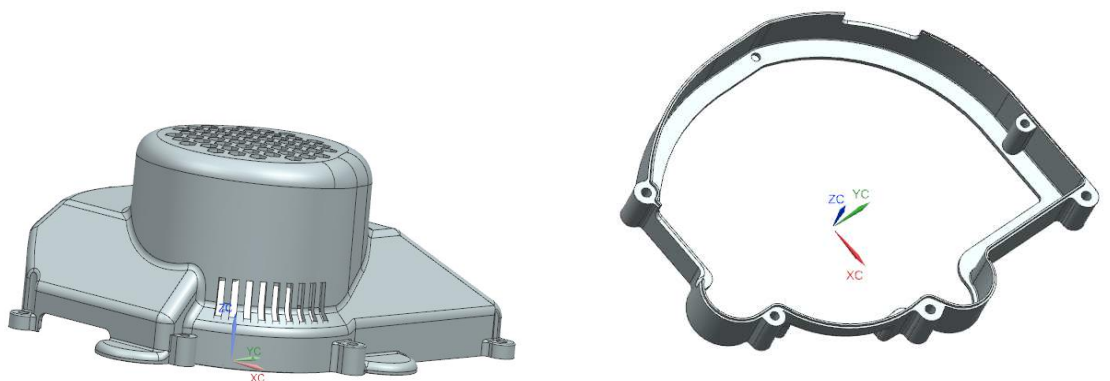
A sinistra il componente superiore. A destra il componente inferiore
